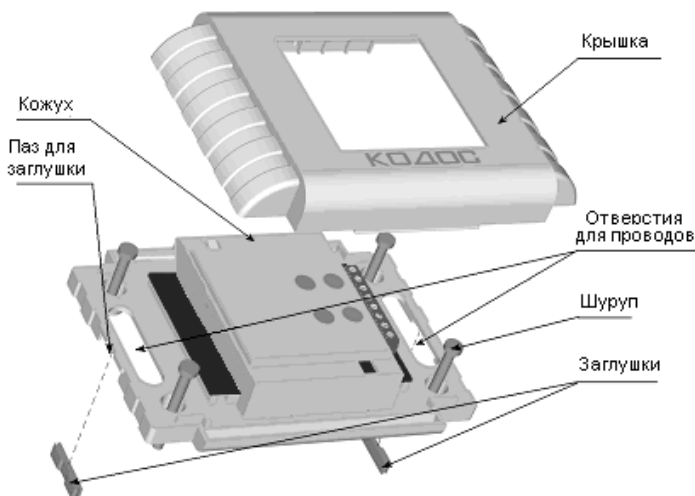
Крепление адресного блока «КОДОС А-09»
